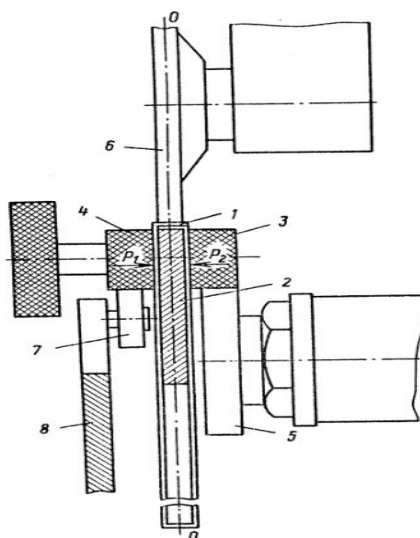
Схема сварки плоской трубчатой детали
